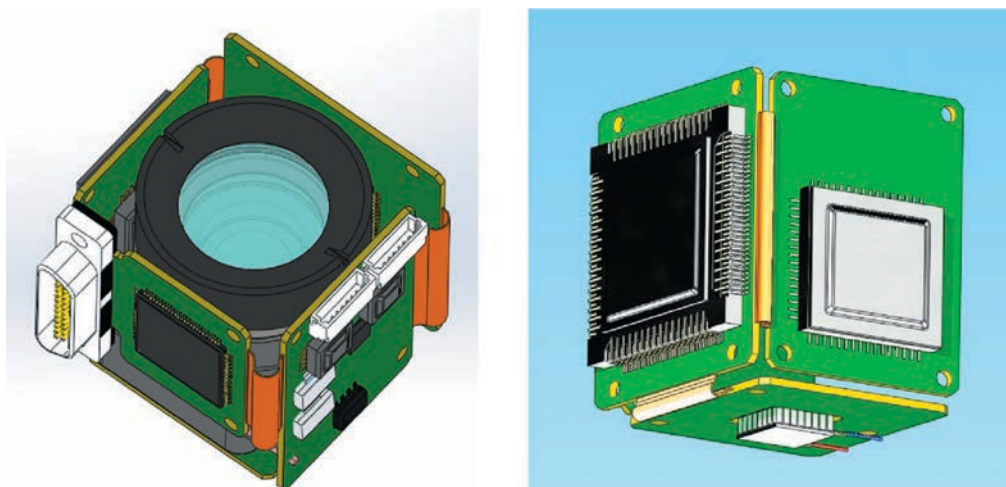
Гибко-жесткая плата, свернутая в куб для установки в корпус звездного датчика
